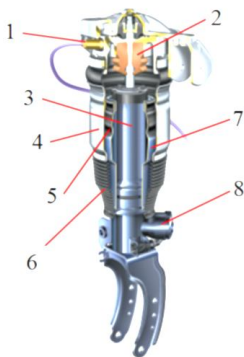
Модуль пневматичної стійки системи активної підвіски CDC: 1 – клапан підтримання залишкового тиску; 2 – додатковий пружний елемент; 3 – амортизатор; 4 – зовнішня направляюча; 5 - рукавний елемент; 6 – пильовик; 7 – поршень; 8 – клапан регулювання демпфування (CDC)
